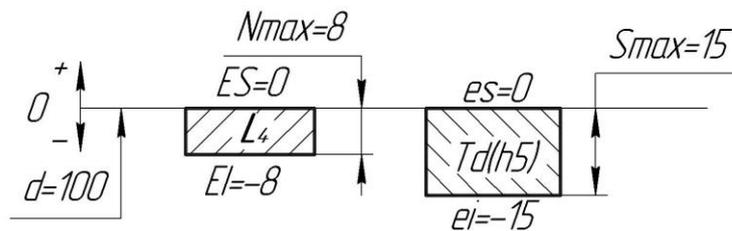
Схема розташування полів допусків внутрішнього кільця підшипника на вал.
